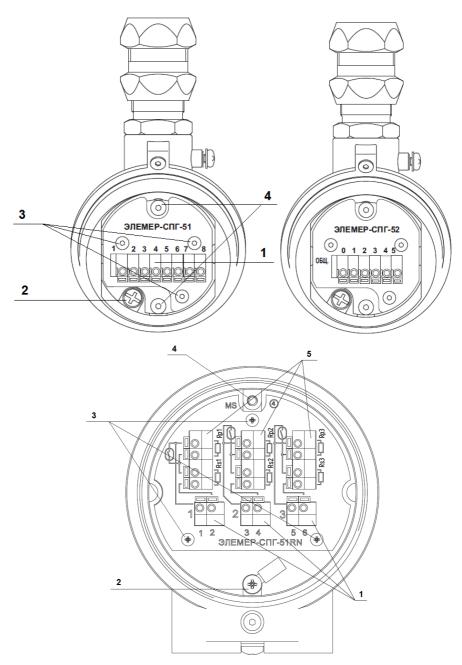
Монтажные платы с клеммными блоками (крышка корпуса снята)
